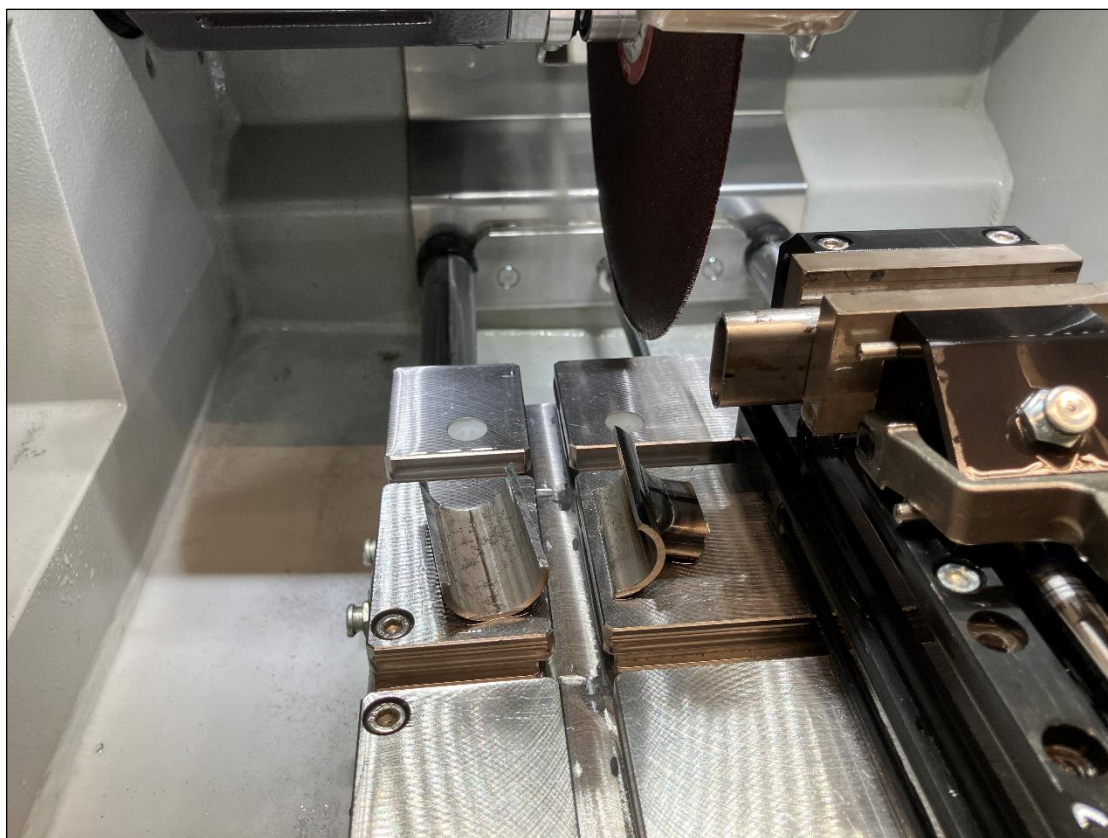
Ein- oder beidseitig geschweißter Bügel nach Schnitt 1 und 2.
